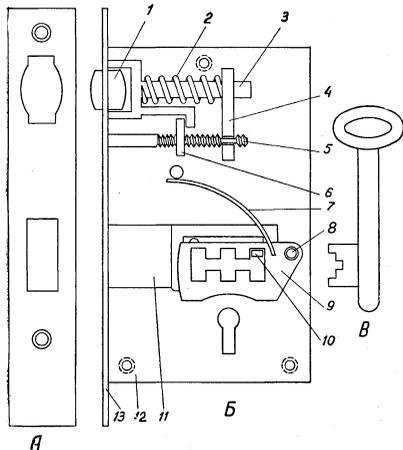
Устройство врезного дверного замка с сувальдным механизмом: А — запорная планка; Б — замок: 1 — ролик защелки (каток); 2 — пружина; 3 — вилка; 4 — упорная планка; 5 — регулировочный винт; 6 — регулировочная планка (гайка винта); 7 — пружина сувальды; 8 — ось сувальд; 9 — сувальда; 10 — стойка засова; 11 — засов; 12 — основание корпуса; 13 — лицевая планка; В — ключ.
